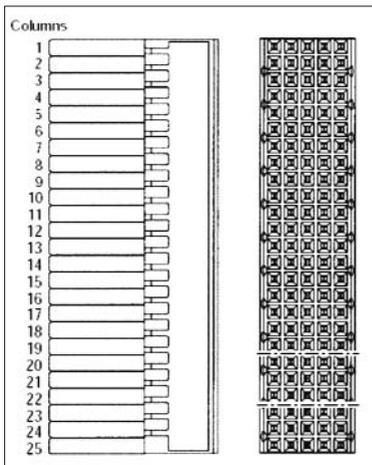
Вид задней панели углового соединителя типа Z-PACK H
